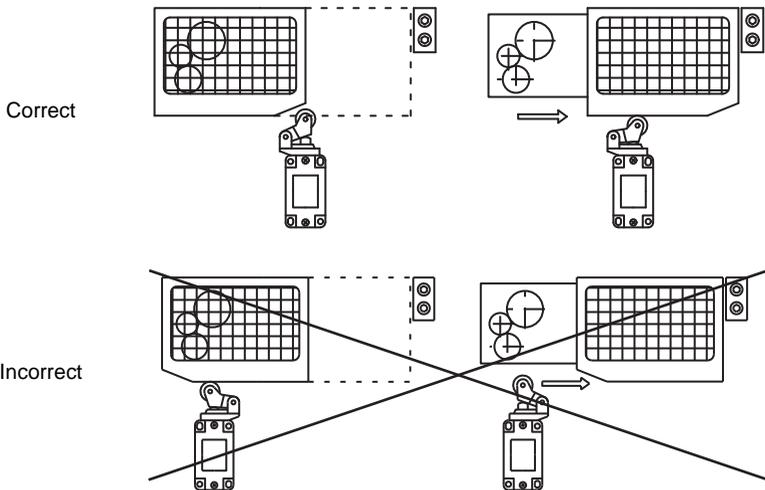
Exemple de montage pour un dispositif de protection coulissant
